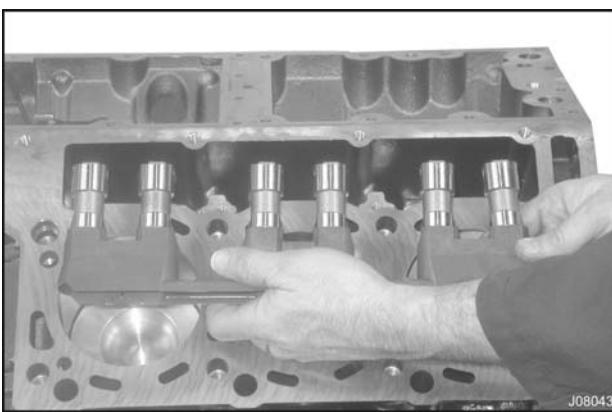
Instalación de los levantaválvulas y de la guía en el bloque
